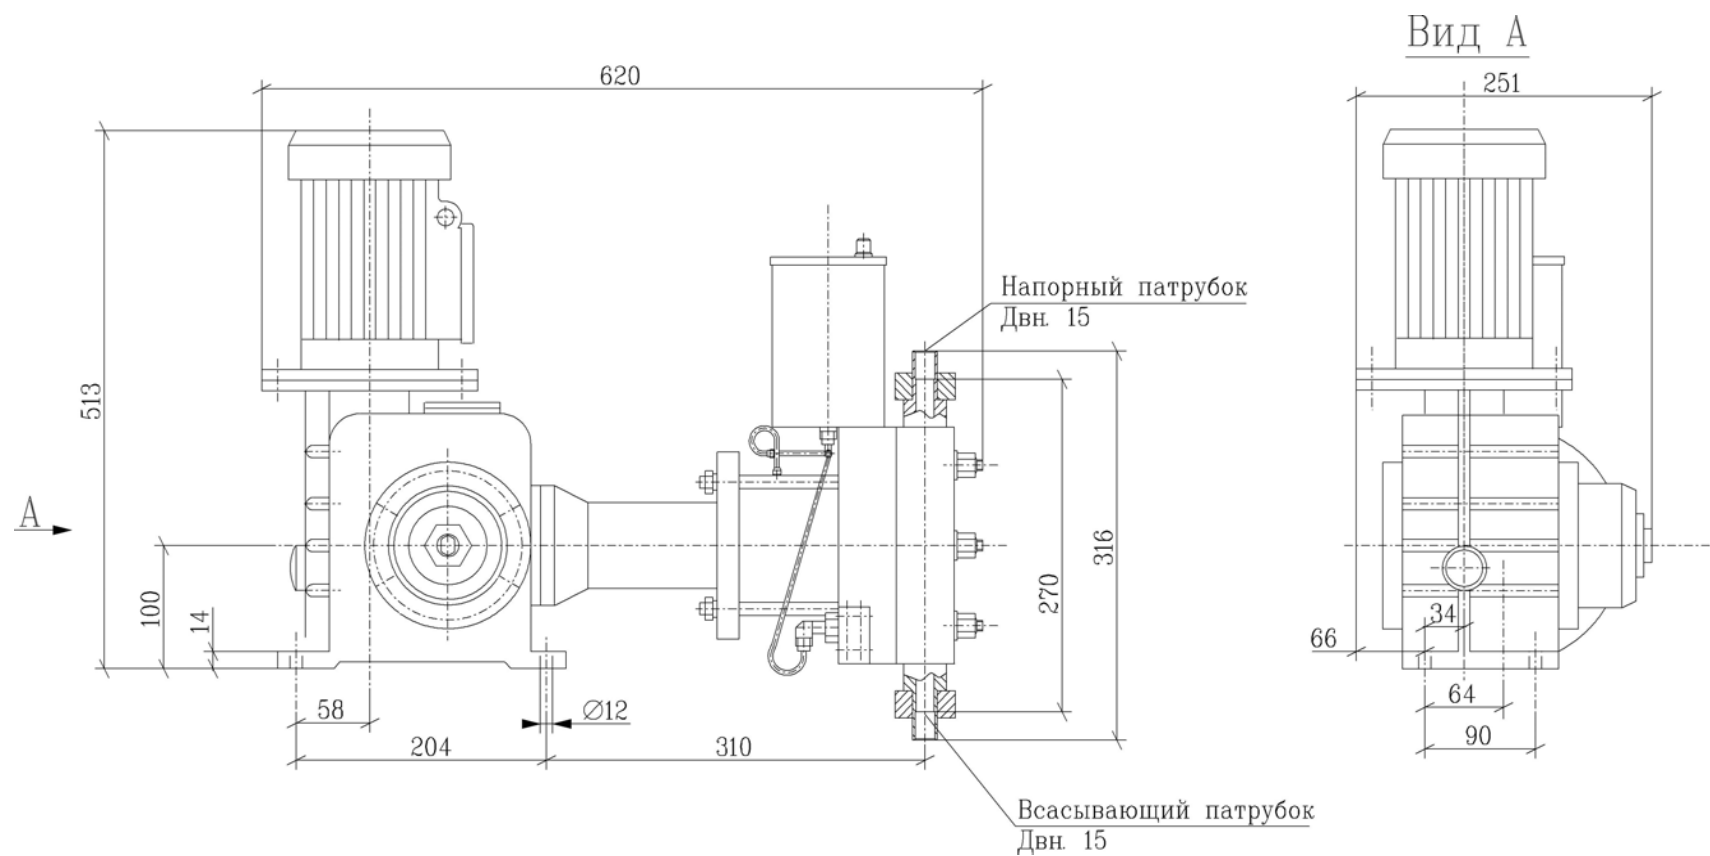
Габаритный чертеж насоса-дозатора фосфата PHN10AP001, PHN10AP002
